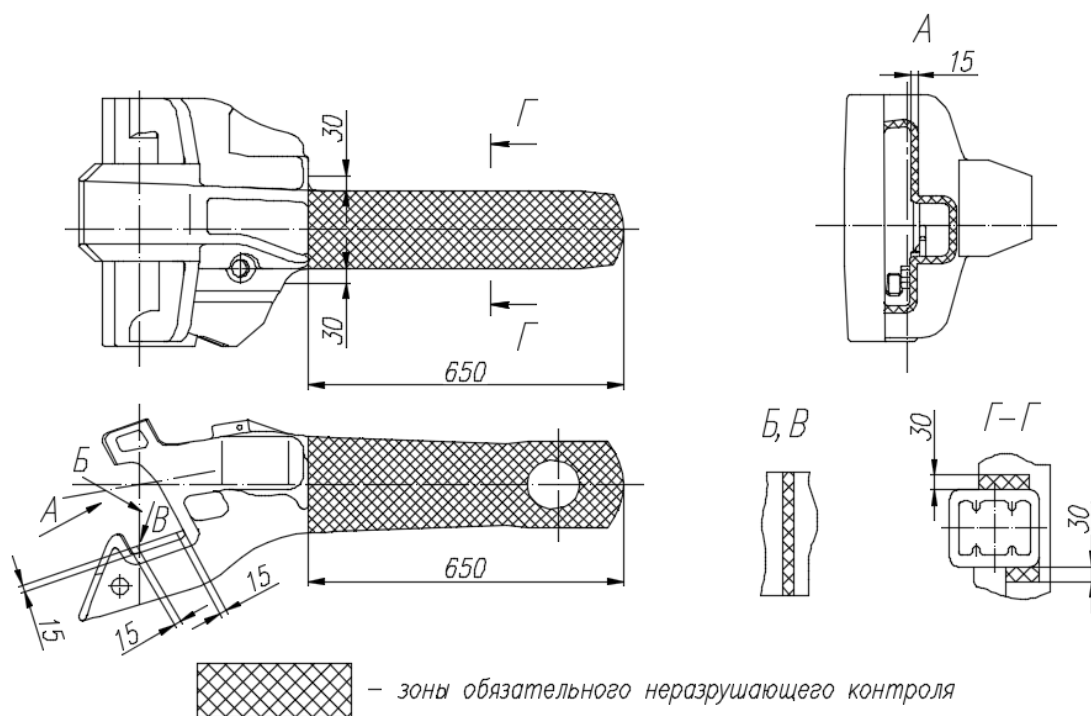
Зоны неразрушающего контроля на корпусах автосцепок ТА-1
